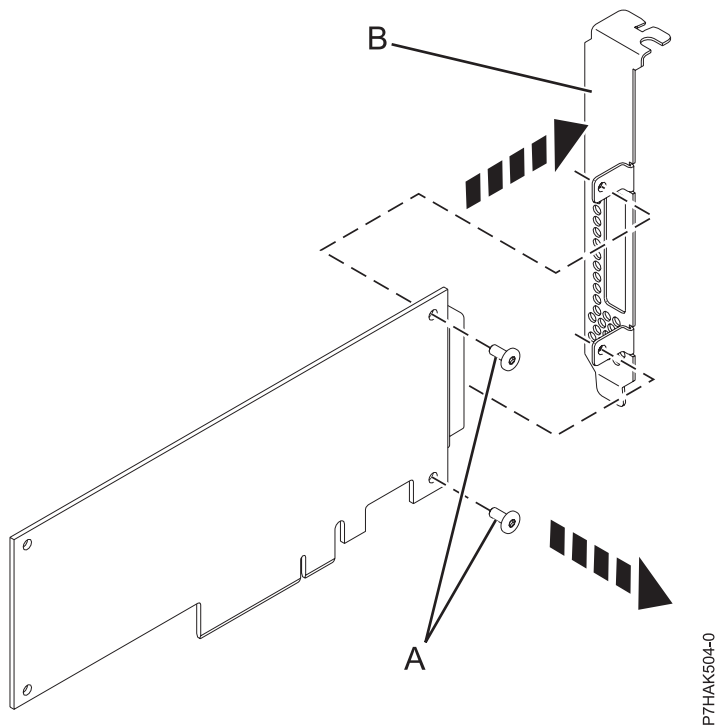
Remover um contraponto de perfil elevado de um novo adaptador PCI
